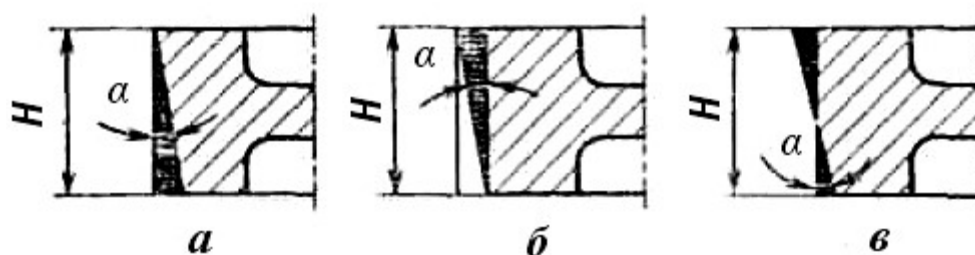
Формовочные уклоны поверхностей: *а* — необрабатываемых, сопрягаемых с другими деталями (за счет уменьшения размера отливки); *б* — обрабатываемых, сверх припуска на механическую обработку (за счет увеличения размера отливки); *в* — необрабатываемых, не сопрягаемых с другими деталями (за счет одновременного уменьшения и увеличения размеров отливки); *H* — высота модели; α — уклон
